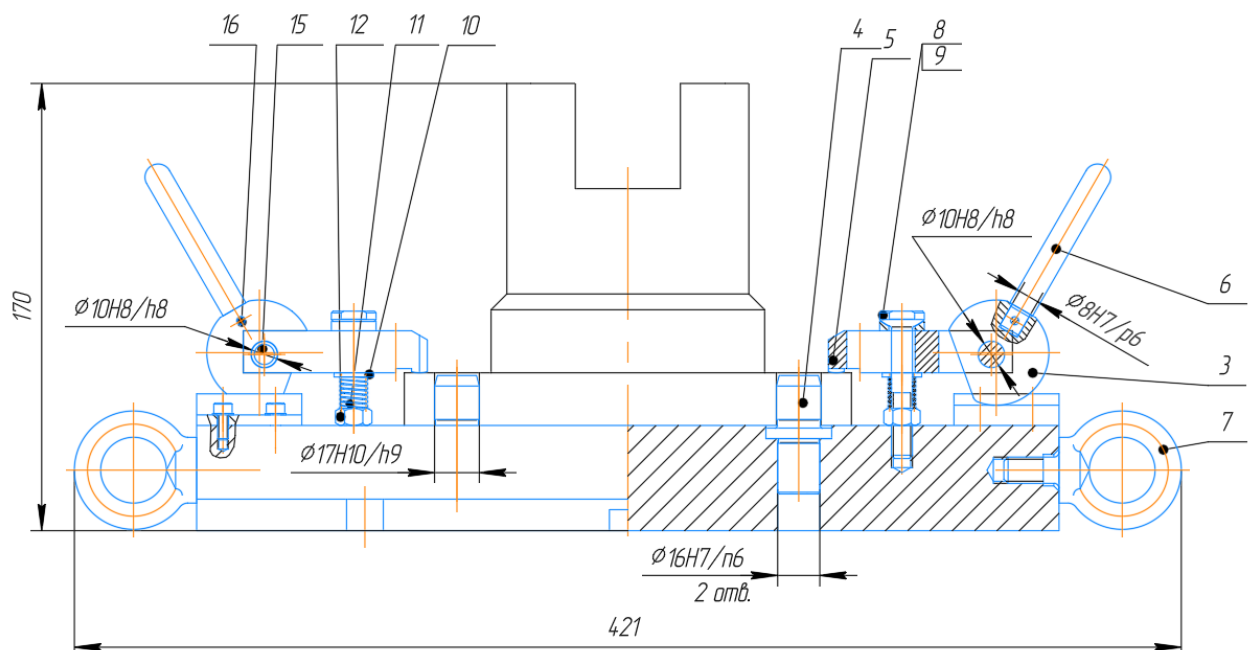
Ескіз пристрою для закріплення деталі на верстаті моделі 6М82Г
